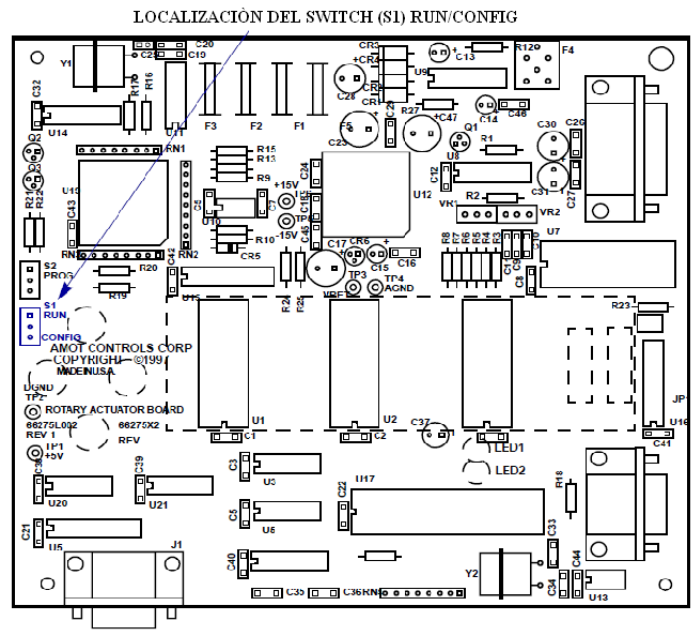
Circuito impreso del controlador (Fuente: Rotary fuel valve and position controller for gas turbines)
